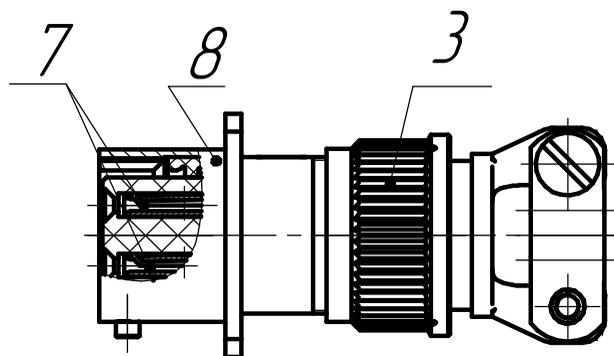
Соединитель ОСН-25- ... Р- ... -12...
